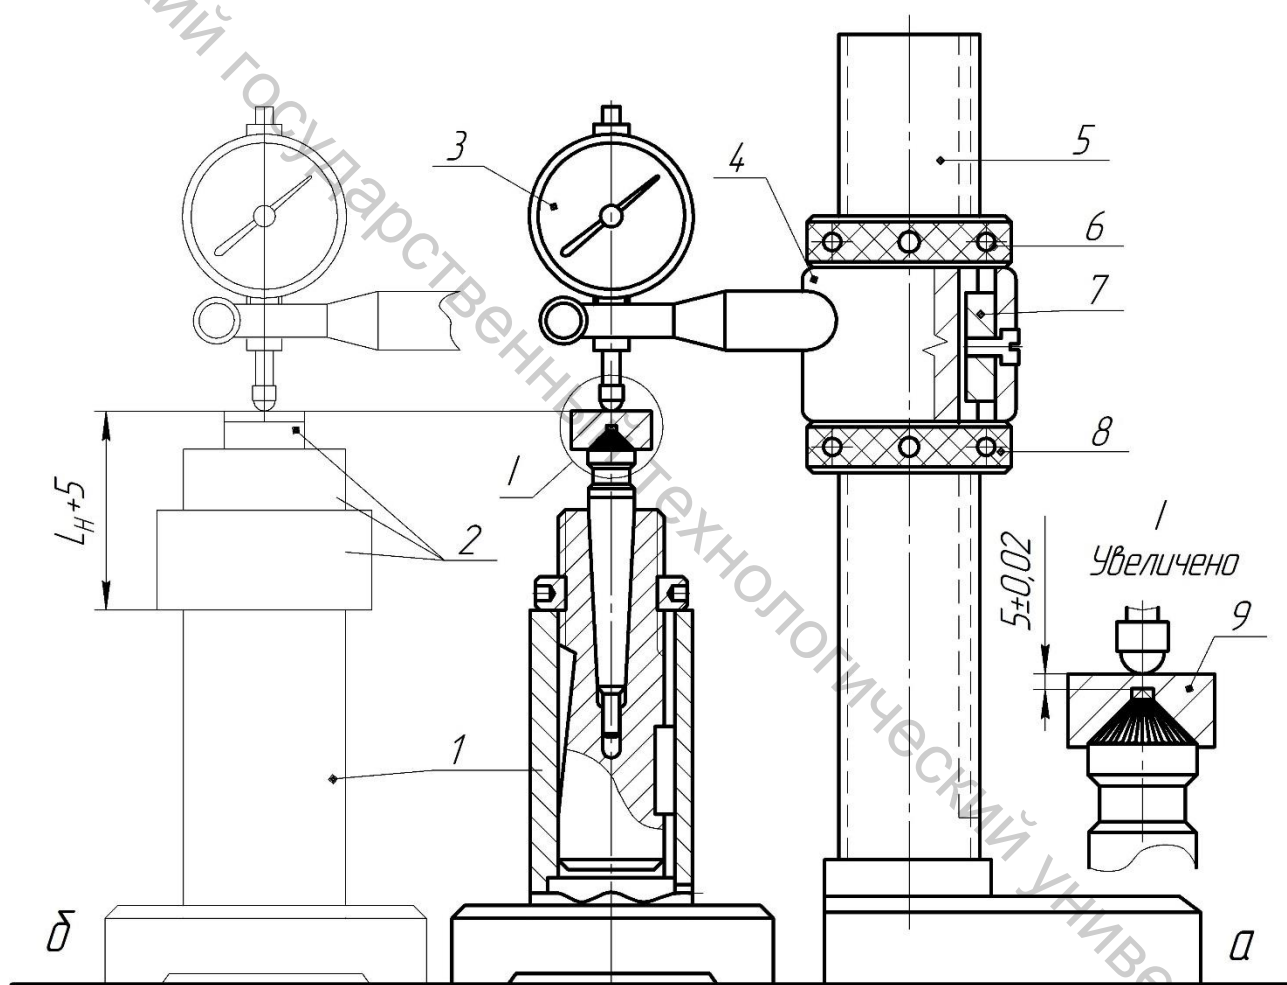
Схемы настройки вне станка зенковки (а) и калибровки средств измерения (б): 1 – стойка, имитирующая шпиндель; 2 – мерные плитки; 3 – индикатор часового типа; 4 – кронштейн индикатора; 5 – стойка индикаторная; 6 и 8 – калибровочные гайки стойки; 7 – шпонка; 9 – проставок-база
